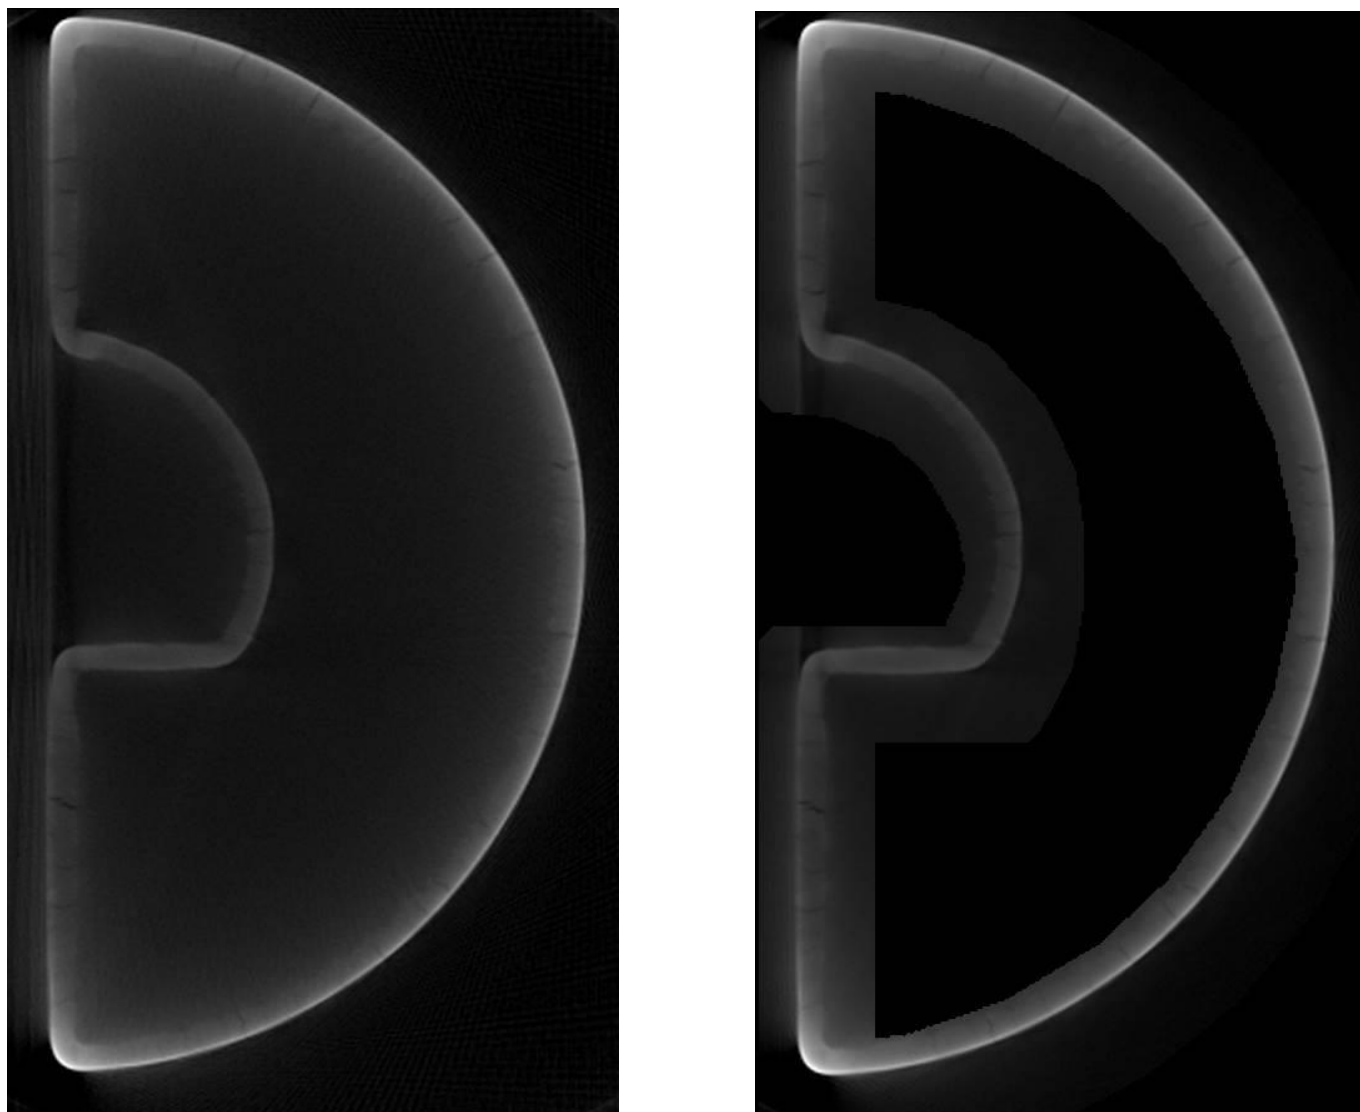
Coupe de la reconstruction de la pièce de fabrication additive par FDK (gauche) et par reconstruction SIRT masquée (droite).
